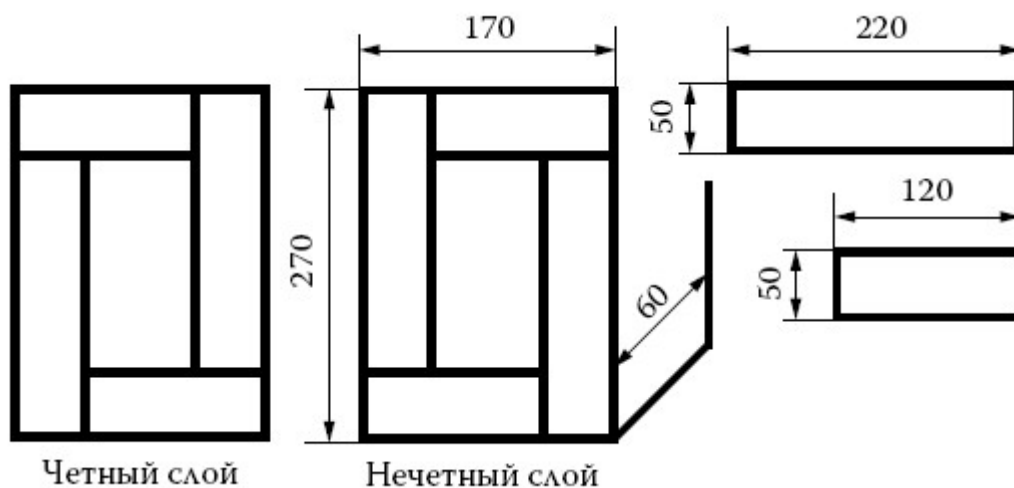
Конструкция самодельного сердечника сварочного трансформатора
